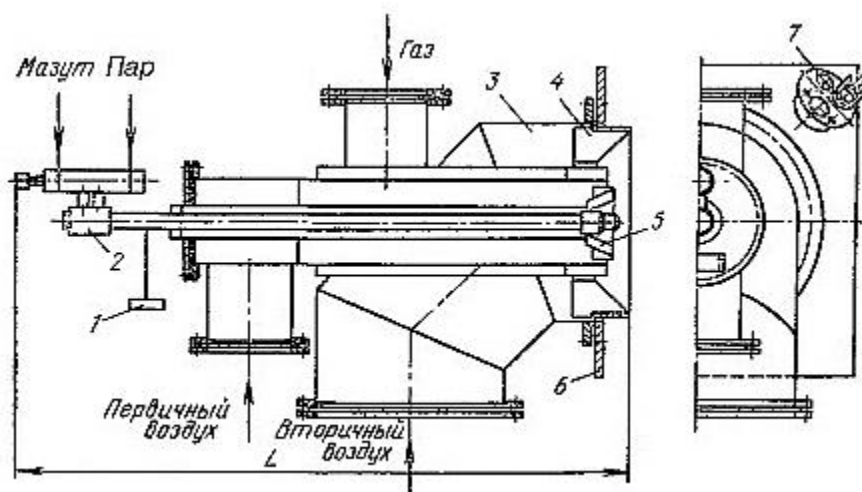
Газомазутная горелка типа ГМГм: 1 – заглушка; 2 – мазутная форсунка; 3 – газоздушная часть; 4 – лопаточный завихритель вторичного воздуха; 5 – лопаточный завихритель первичного воздуха; 6 – монтажная плита; 7 – место установки запальника
